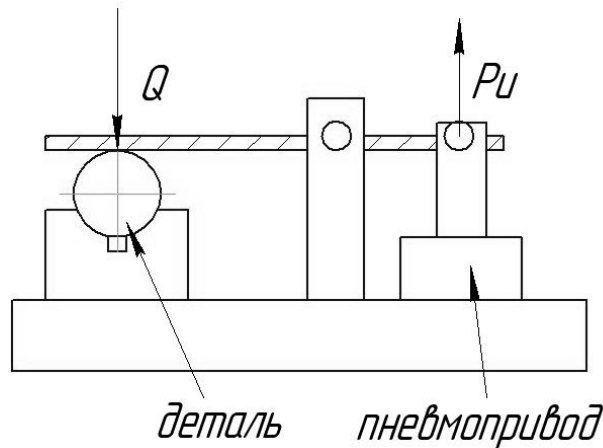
Розрахункова схема сил закріплення заготовки
